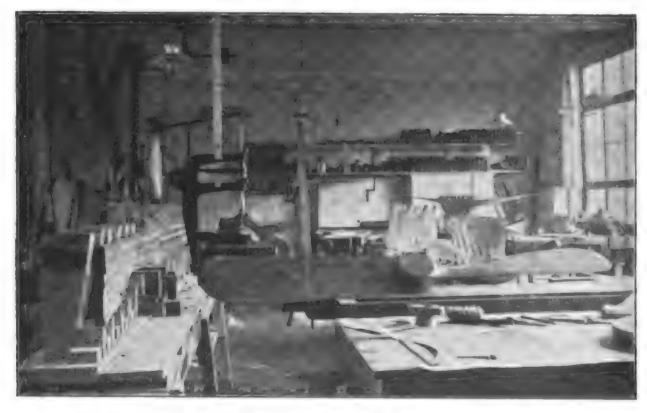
Herstellung der Propeller. Links ein vorgearbeiteter Propeller in der Gabel. Hinten ein Propeller auf der Naben-Bohrmaschine.
